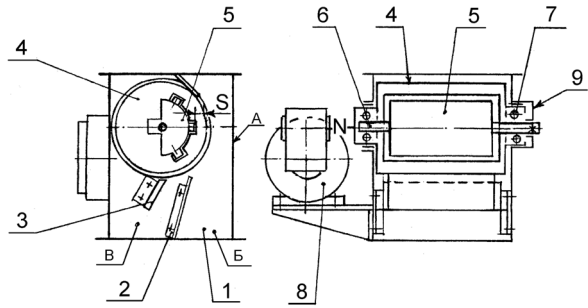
Магнитный сепаратор: 1 - корпус; 2 - перегородка; 3 - скребок; 4 - барабан; 5 - магнитная система; 6, 7 - опоры; 8 - привод
